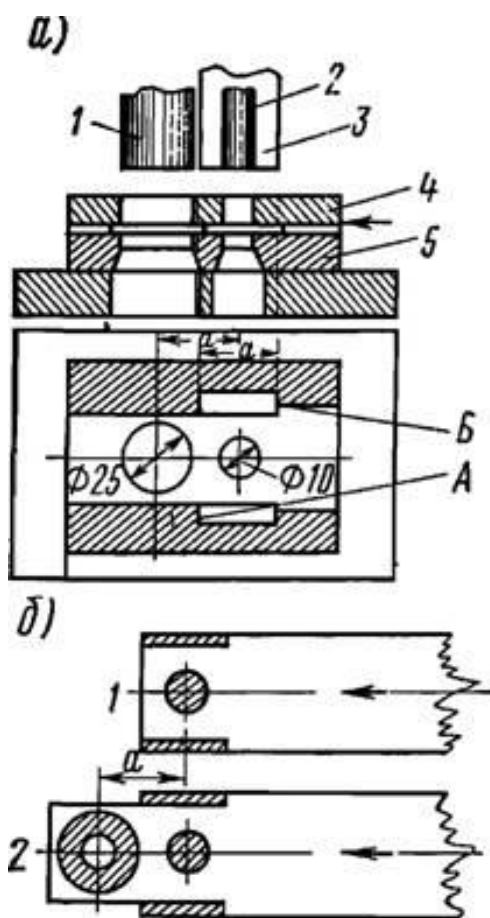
Комбинированный штамп последовательного действия для вырубki шайбы: а — схема устройства штампа; б — схема штамповки
